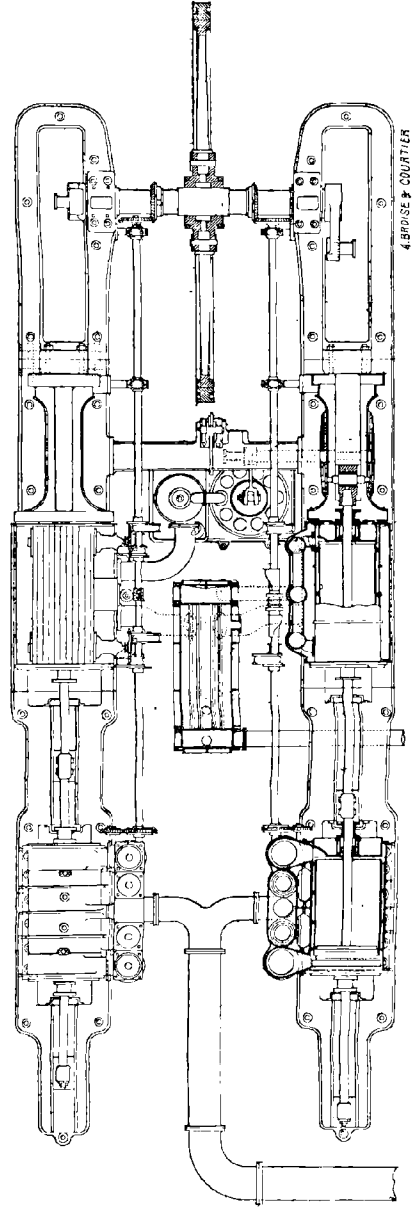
Machine soufflante Riedler à Heft (Carinthie) (plan).
